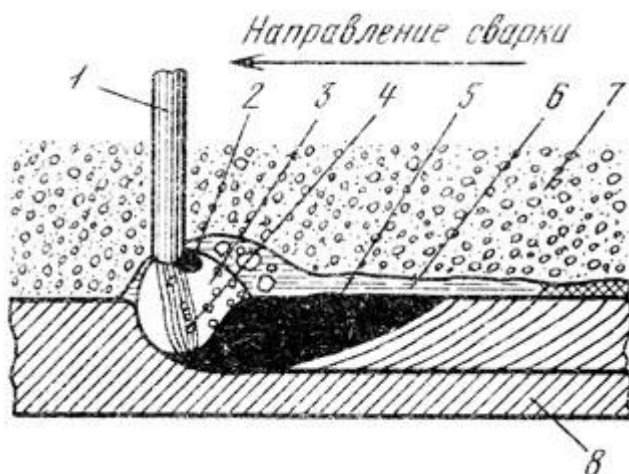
Схема сварки под флюсом: 1 - электродная проволока, 2 - образующаяся капля, 3 - газовый пузырь, 4 - дуга, 5 - сварочная ванна, 6 - расплавленный флюс, 7 - нерасплавленный флюс, 8 - изделие
